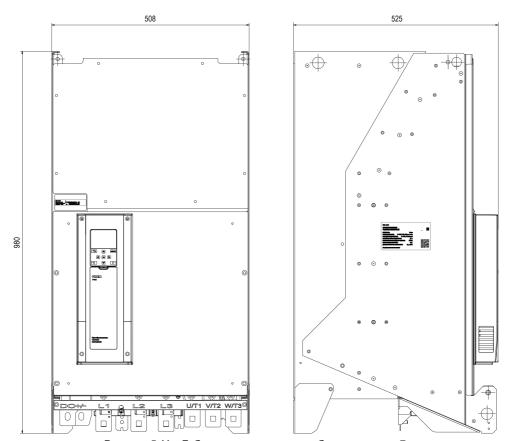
Габаритные размеры прибора в корпусе 7
